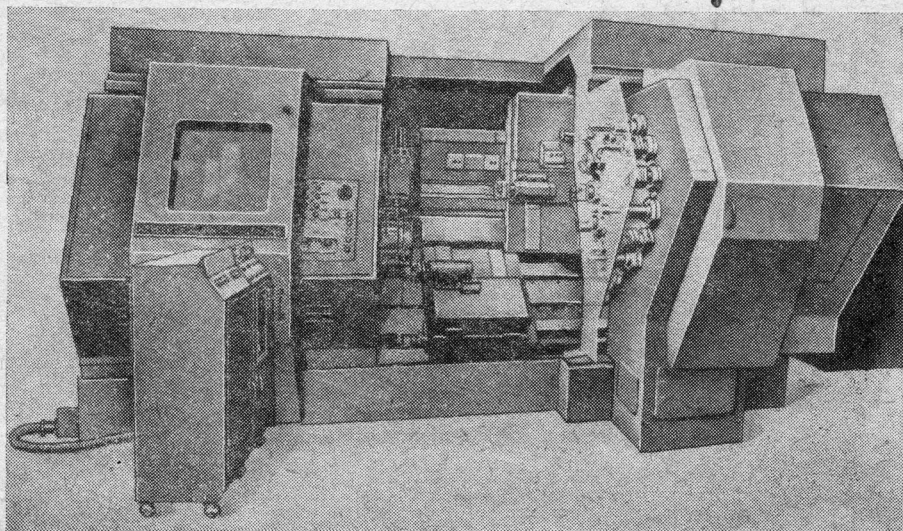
Токарный «обрабатывающий центр» фирмы «Herbert»
